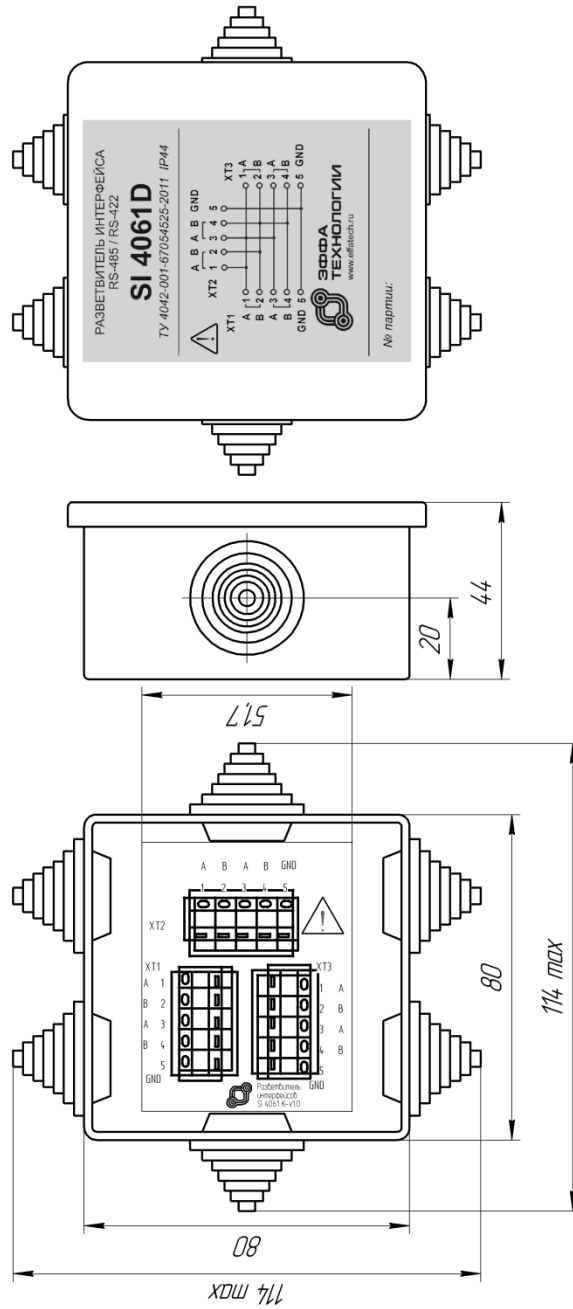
Габаритные и установочные размеры разветвителя SI 4061D
